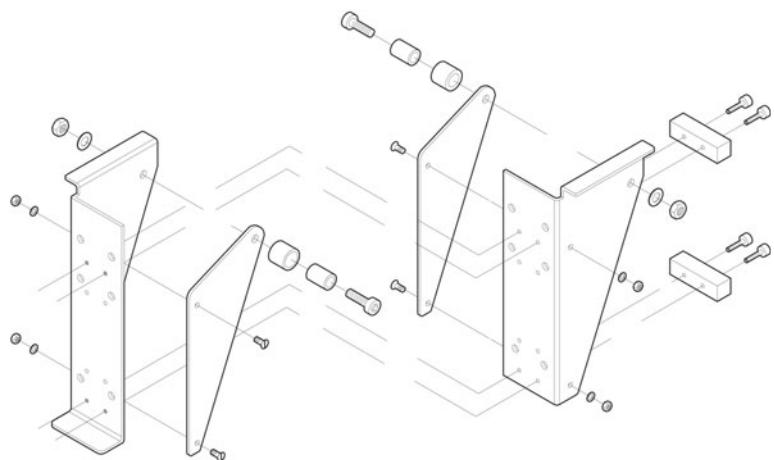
Explosionszeichnung einer Pumpenhalterung (Brüsehaber)
